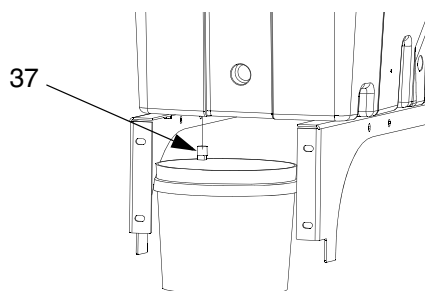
Collocazione del secchio sotto il tappo di drenaggio
